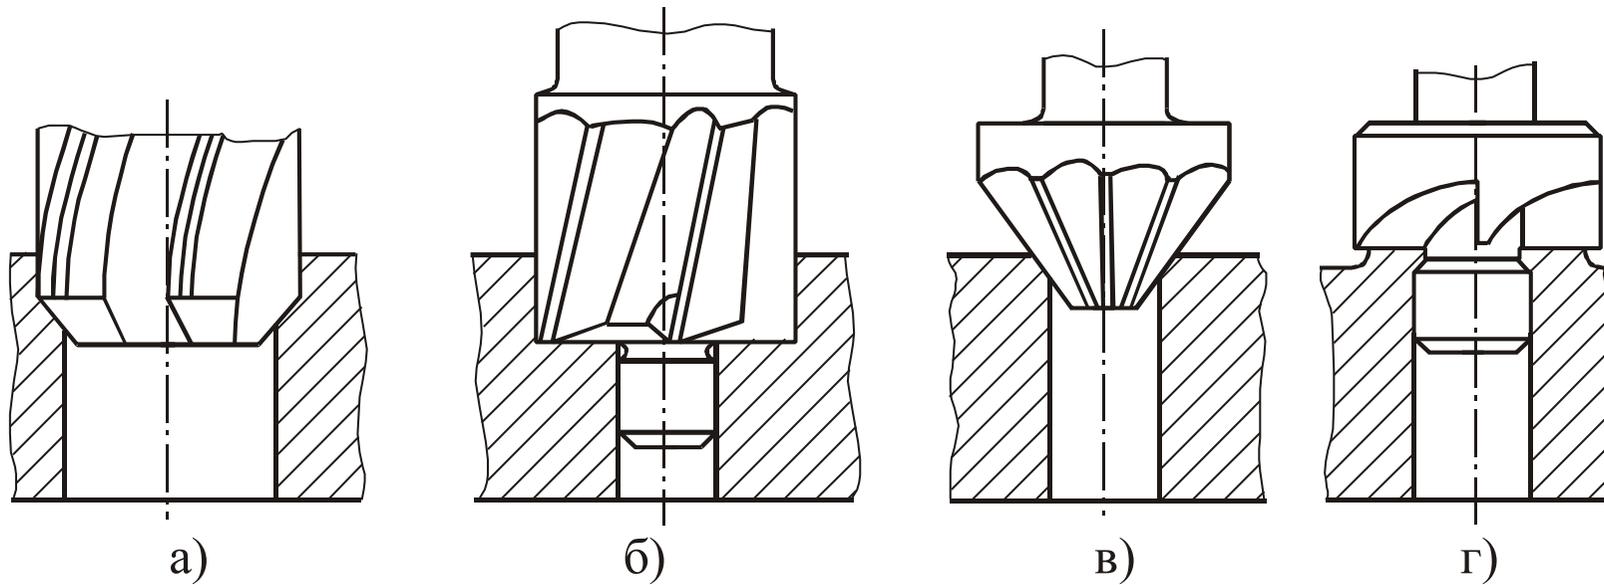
Типы зенкеров: *a* – цилиндрический зенкер; *б, в, г* – зенковки
